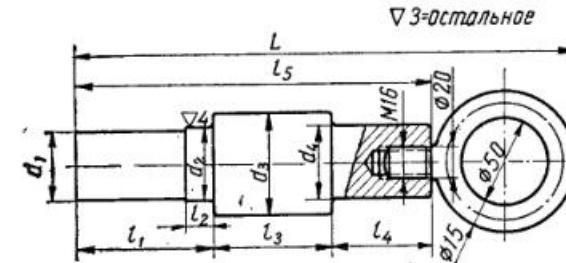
Приспособление для подъема крышек двигателей типов NVD-48 и NVD-36.
